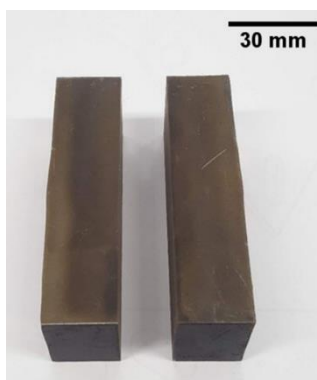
Corte por eletroerosão separando o pino e a rebarba sobressalente do restante da junta soldada.
